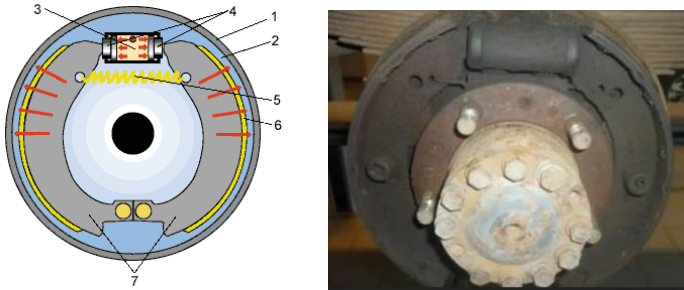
Барабанный гальмівний механізм: 1 – гальмівний барабан; 2 – гальмівний щит; 3 – робочий гальмівний циліндр; 4 – поршні робочого гальмівного циліндра; 5 – стяжна пружина; 6 – фрикційні накладки; 7 – гальмівні колодки
